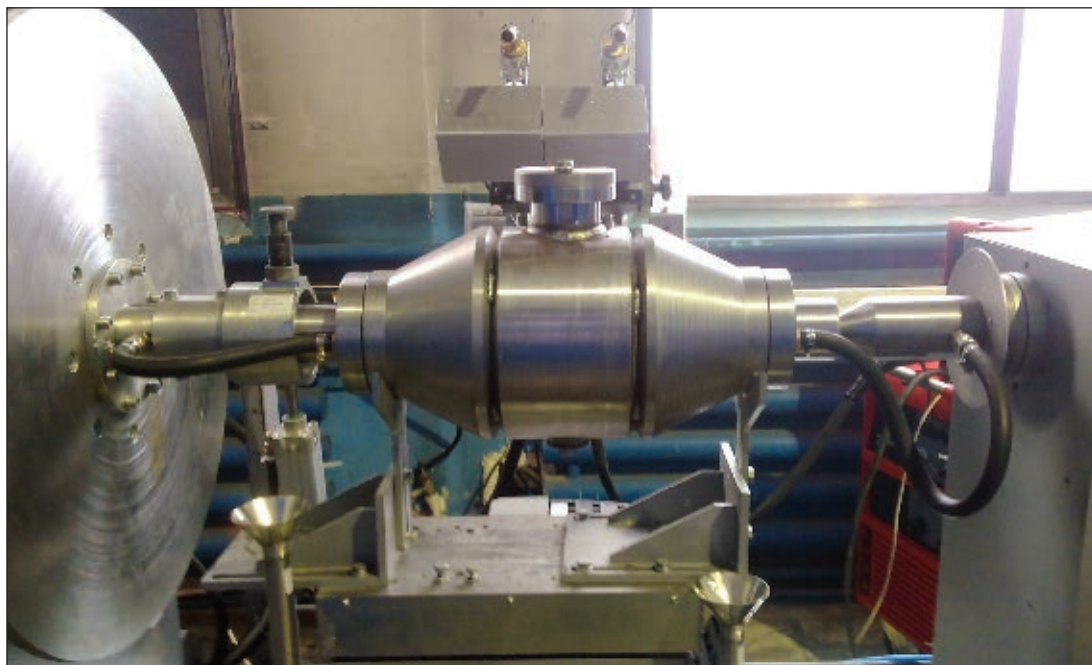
Подготовленный для сварки корпус шарового крана с подводом охлаждающей воды
